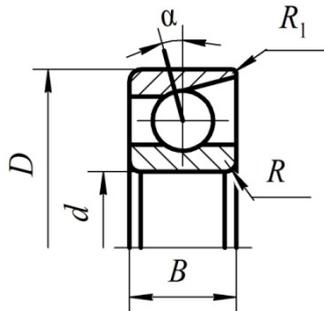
Габаритные размеры шариковых радиально-упорных подшипников
